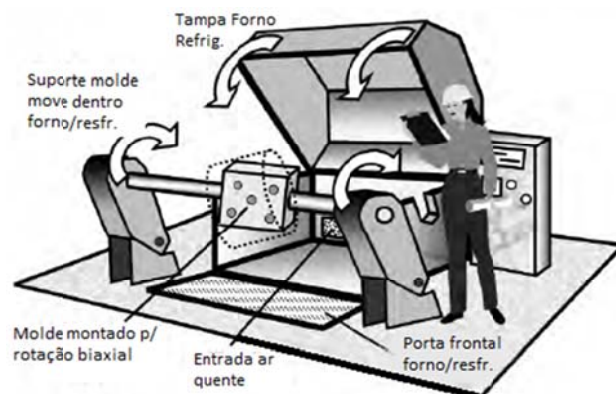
Máquina de rotomoldagem do tipo concha (*clamshell*).
